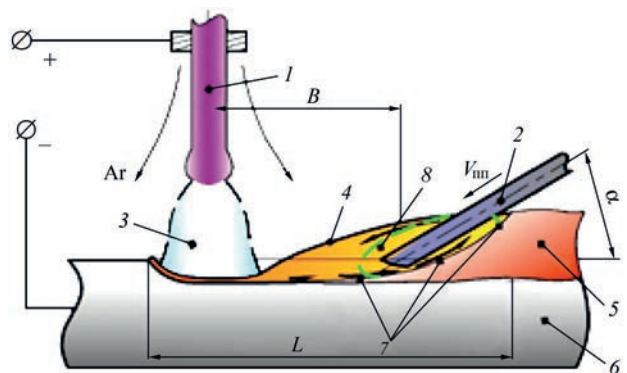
Схема введення присадного модифікованого порошкового дроту у зварювальну ванну в процесі електродного наплавлення [16]: 1, 2 – електродний й присадний порошок дроти; 3 – електрична дуга; 4 – зварювальна ванна; 5, 6 – наплавлений і основний метали; 7 – фронт кристалізації наплавленого металу; 8 – переохоложена зона металевого розплаву
